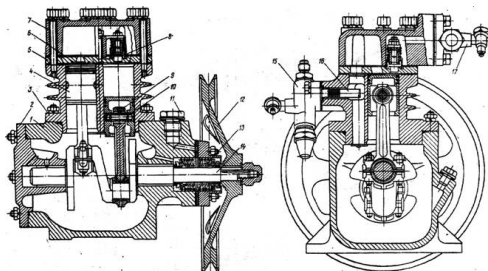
Двопоршневий фреоновий компресор ФВ-0,7 (2ФВ-4/4,5)
